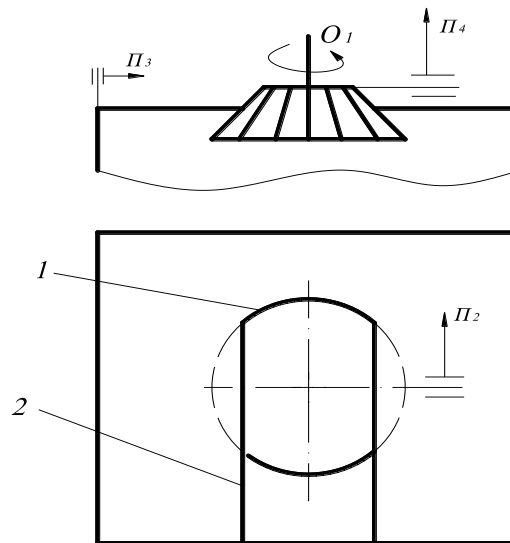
Схема фрезерування «ластівкового хвоста» фасонною фрезею
